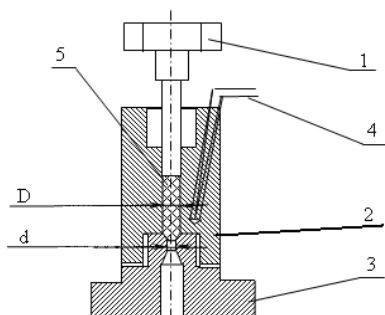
Ячейка высокого давления: 1 - пуансон; 2 - матрица; 3 - основание; 4 - термopар; 5 - заготовка композиционного материала, D - диаметр исходного образца, d - диаметр фильеры.
